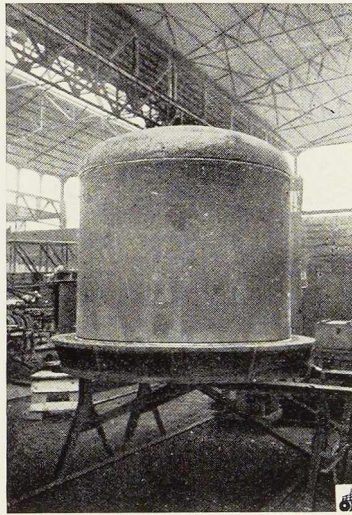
Cuve montée verticalement pour l'exécution des soudures d'assemblage des brides sur la cuve.
